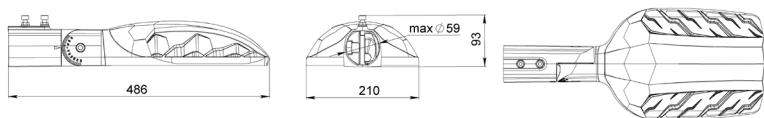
Общий вид светильника Street 9M с консольным поворотным креплением.
